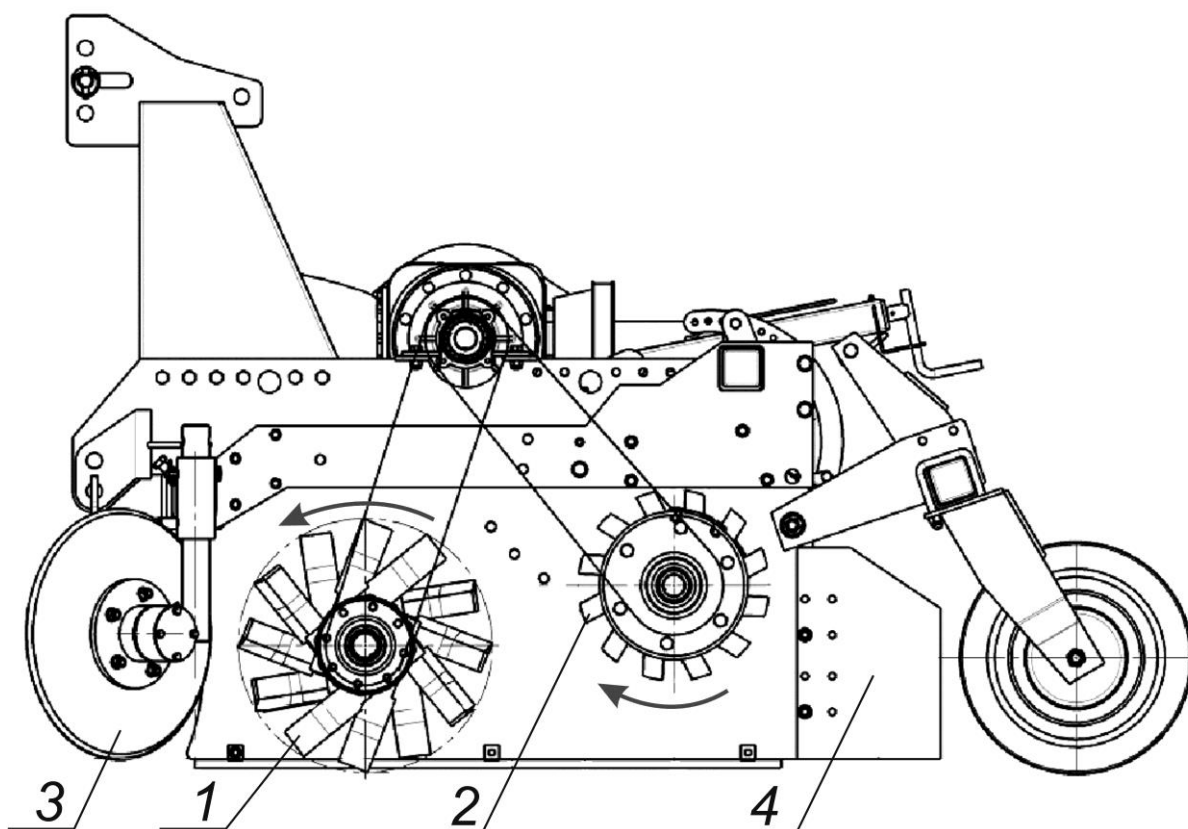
Фрезерный двухроторный культиватор ФГФ-1 для нарезки гряд
